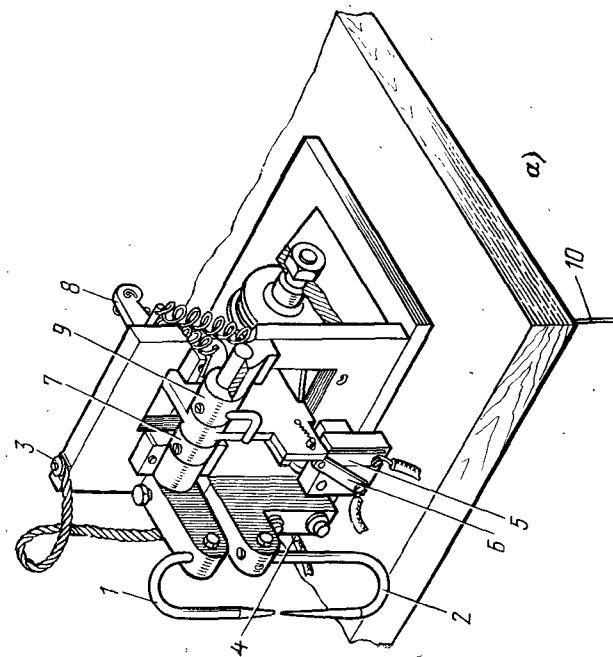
Прессик и сварочная головка монтажного стола.
